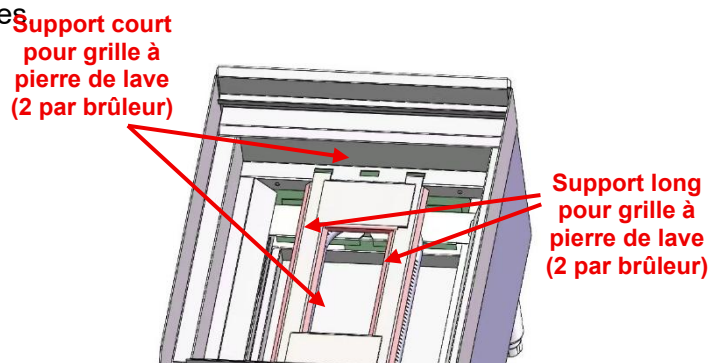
Figure B – Supports longs et courts pour grilles à pierre de lave correctement installés.
